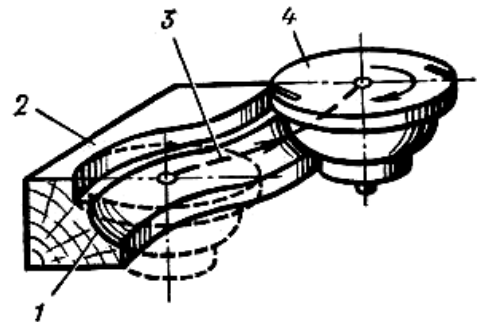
Формирование профиля двоякой кривизны на фрезерном станке:
